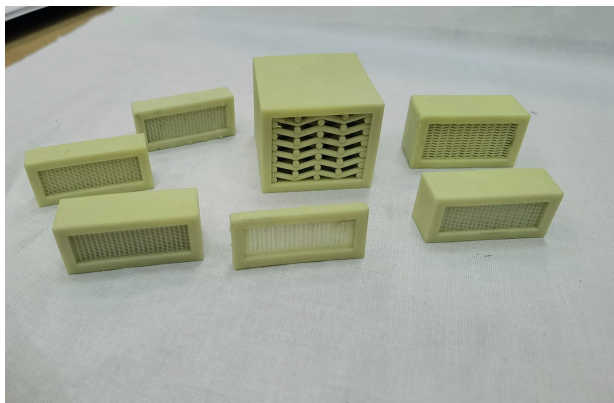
Внешний вид образцов из ФМТС, изготовленных с частью корпуса
